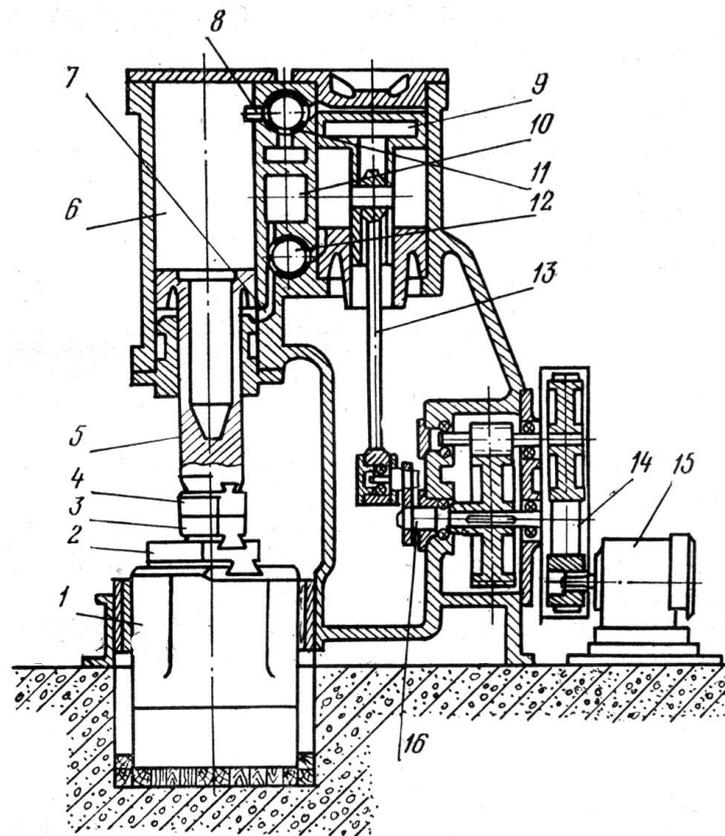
Пневматический двухцилиндровый одностоечный ковочный молот двойного действия
